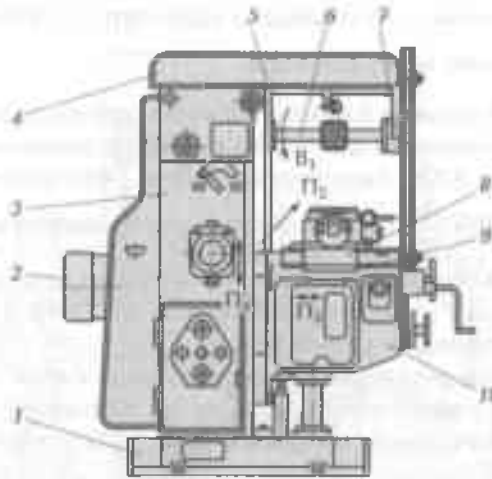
Горизонтальный консольно-фрезерный станок:
